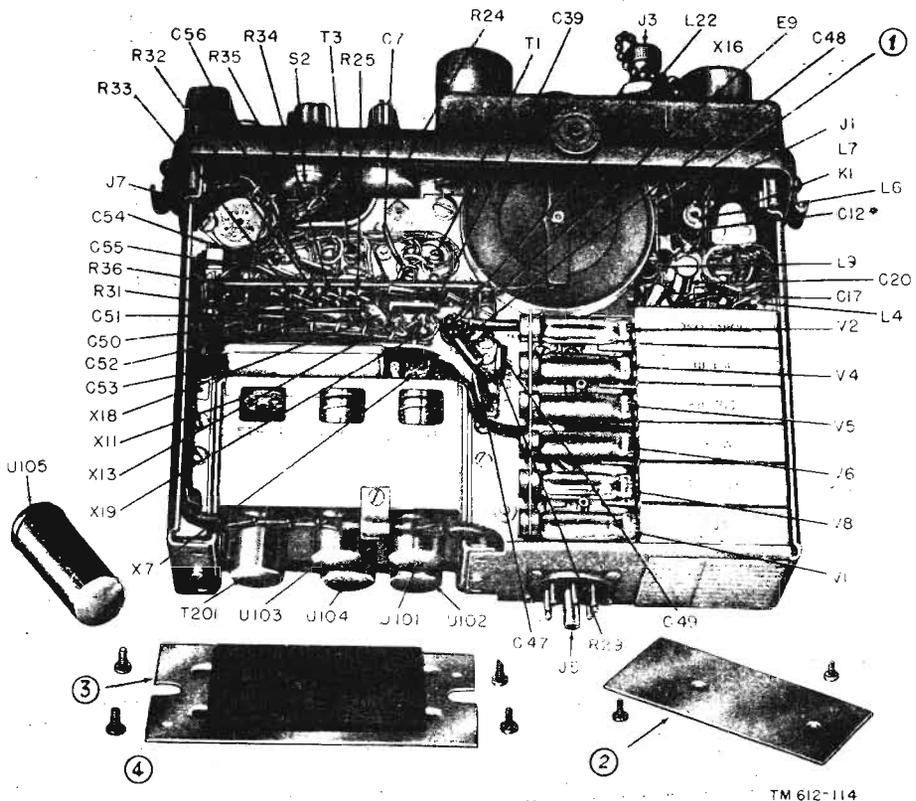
Chassis del ricetrasmettitore, visto di sopra.
